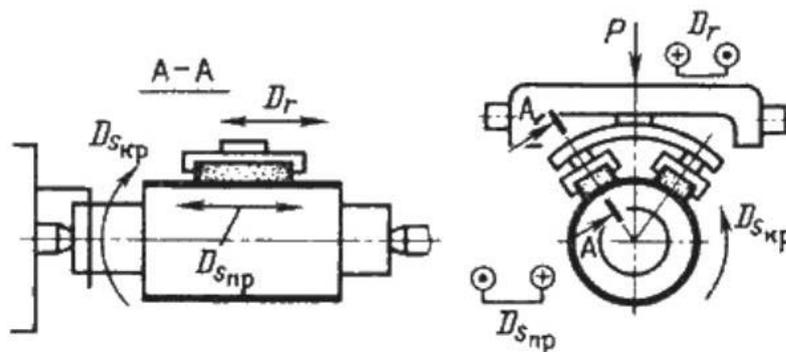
Схема суперфиниширования цилиндрической поверхности
